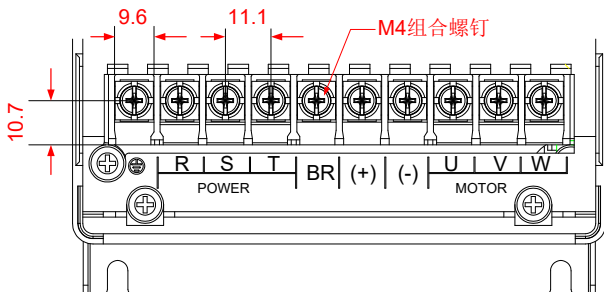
3.7kW~5.5kW 功率等级的接线端子尺寸图 (单位: mm)
